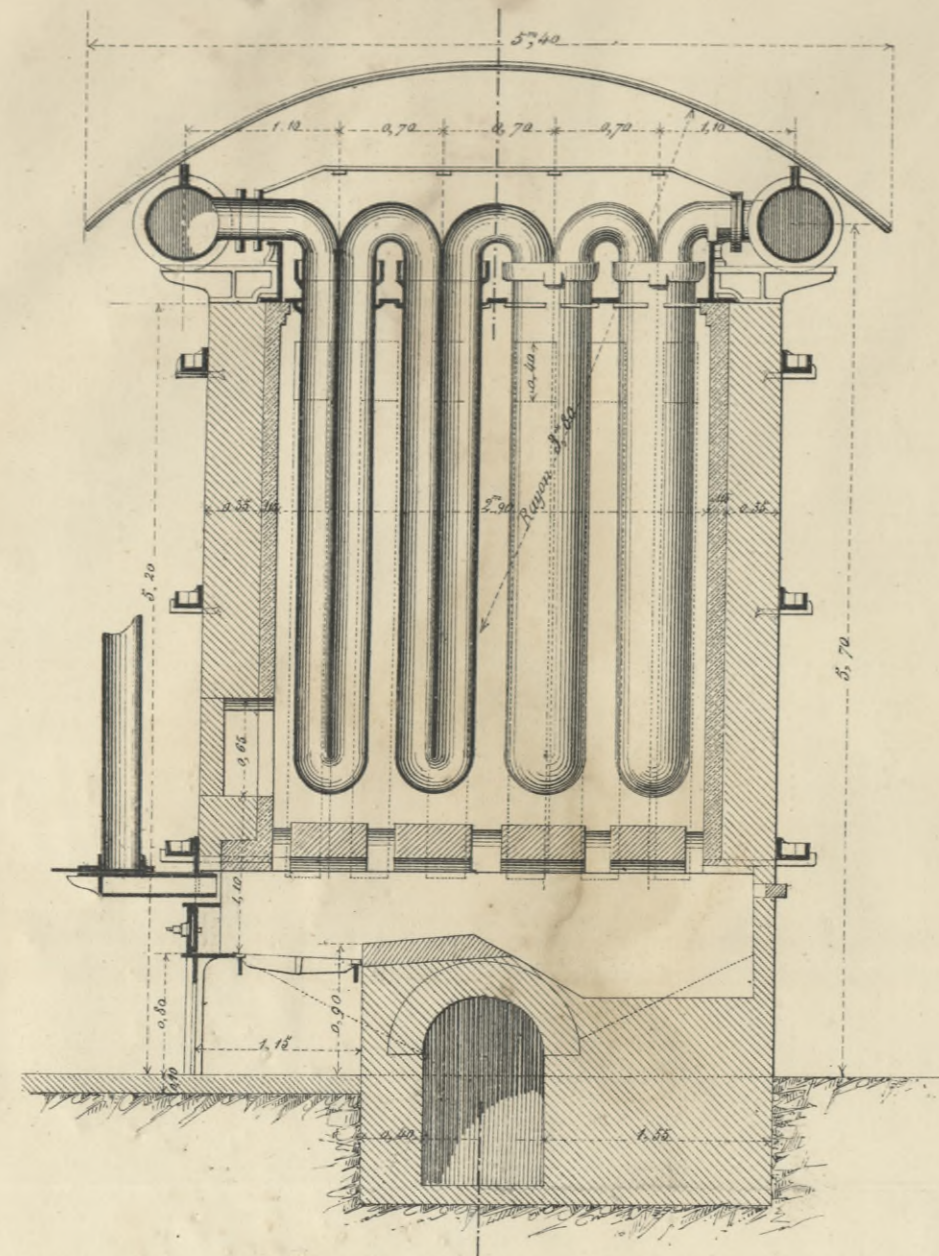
Elevation et Coupe longitudinale à 0,02 pour 1⁰⁰⁰.
